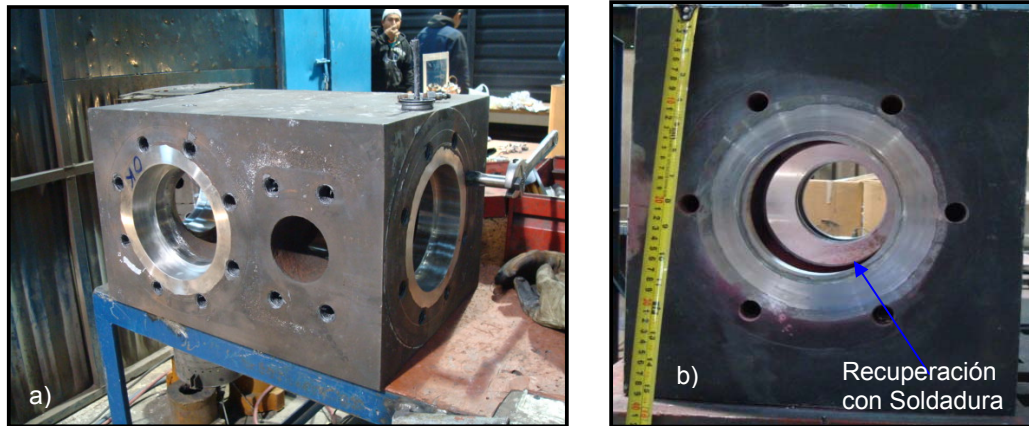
Equipo mecanizado para la aplicación de la soldadura GMAW.
